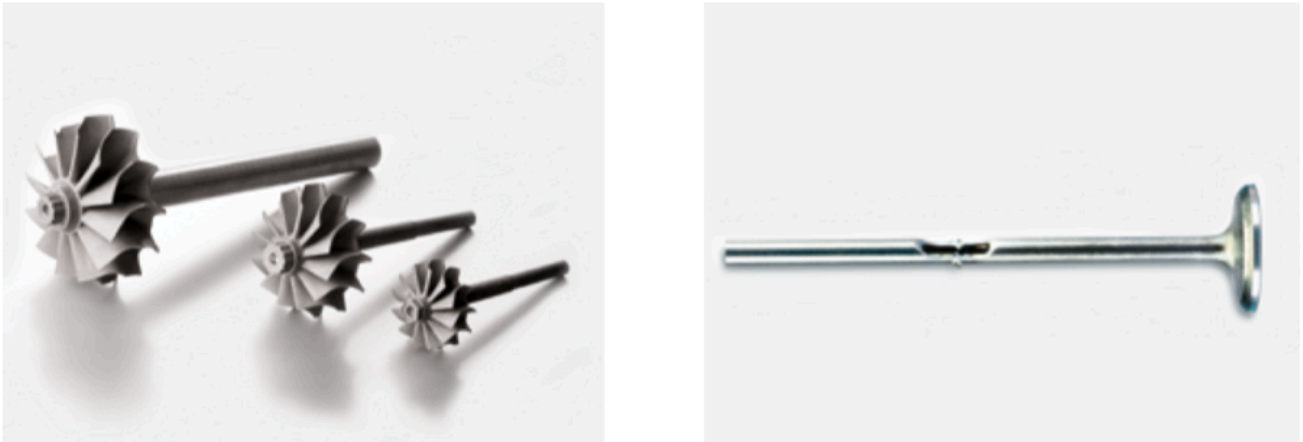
Turbinas-ejes (izq.) y válvulas huecas (der.) soldados mediante RFW. [31]
